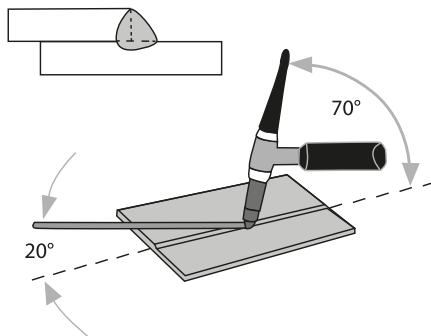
Положення «TIG-пальника» під час виконання зварювання з'єднання внапусток.
